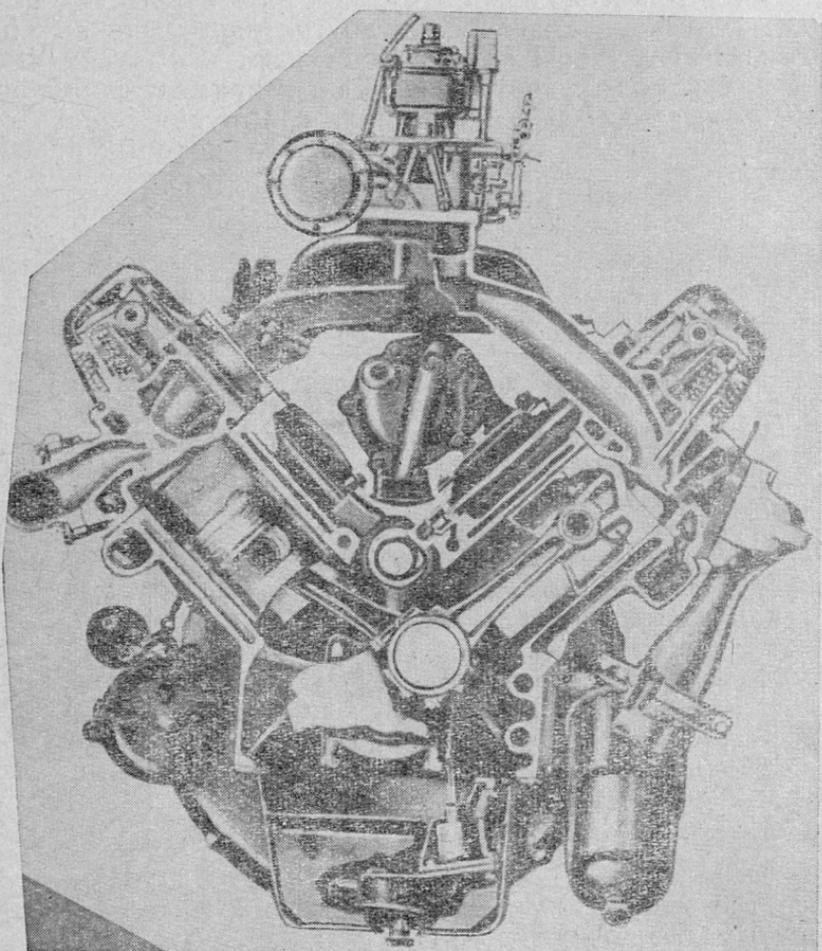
Поперечный разрез V-образного 8-цилиндрового карбюраторного двигателя International-Harvester
